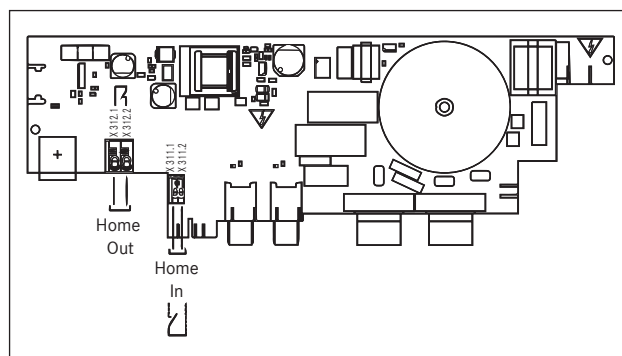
Schema di collegamento contatti di commutazione esterni
